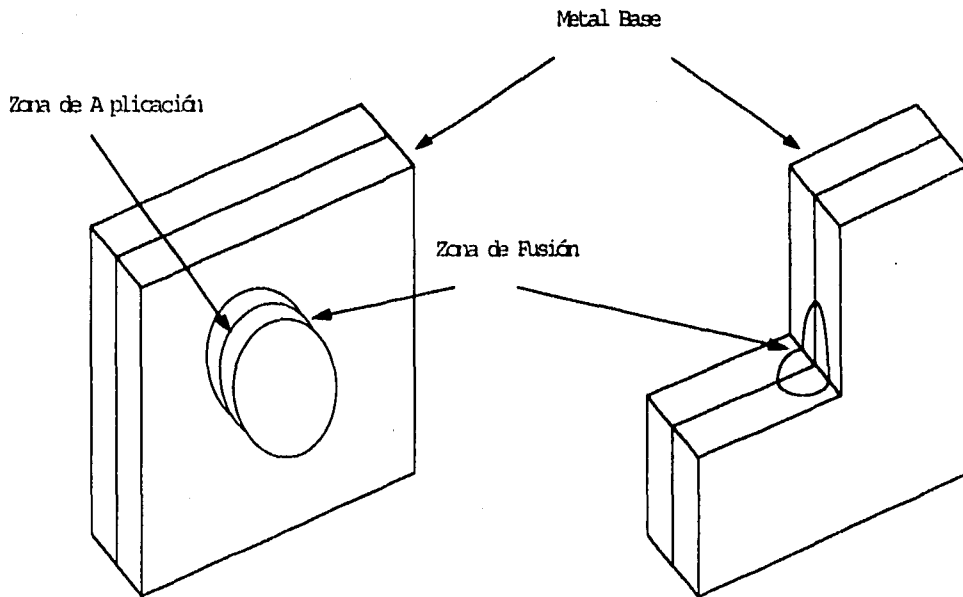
Piezas terminadas al ser soldadas por el proceso de soldadura por puntos.
